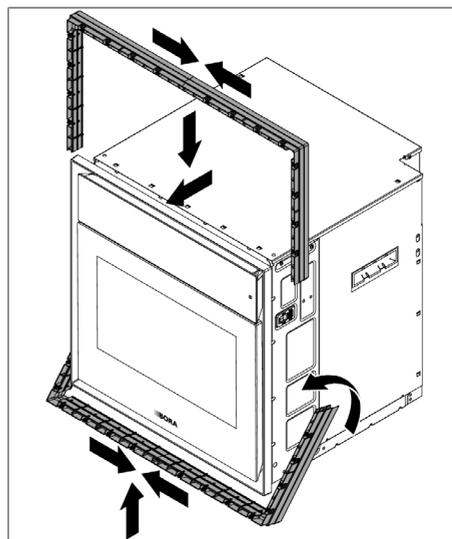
Montagem de 2 estruturas de espaçamento
